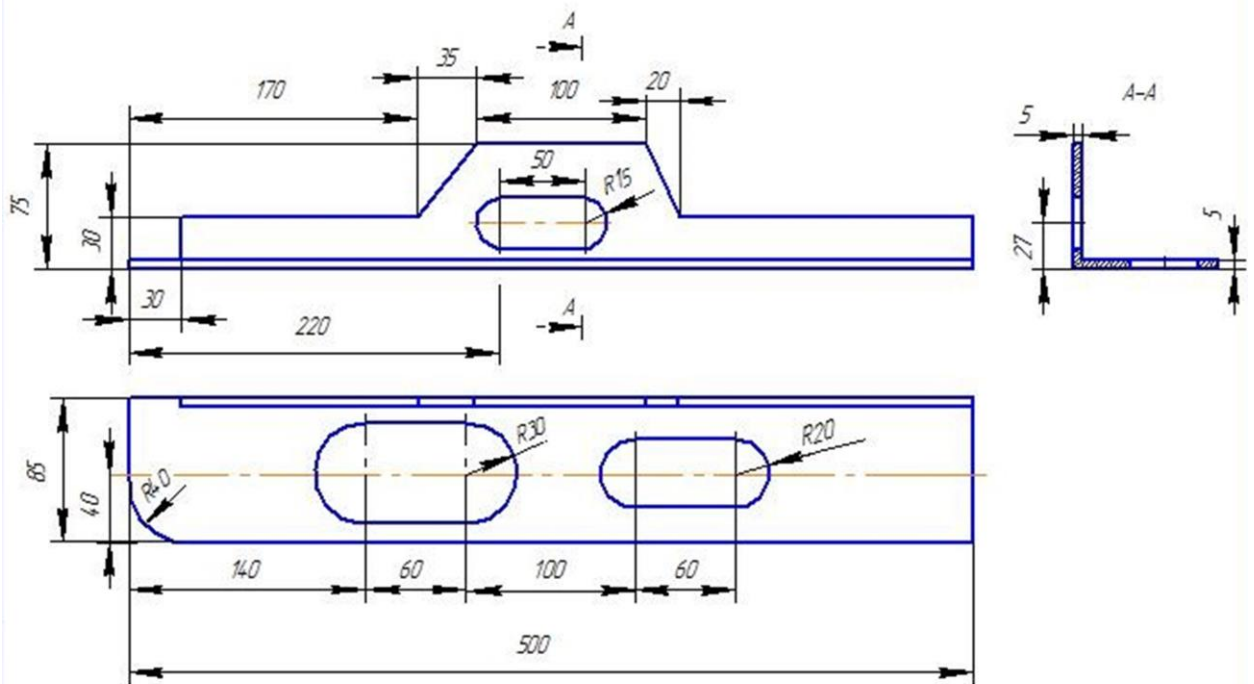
Эскиз 2 образца с различным сочетанием поверхностей
